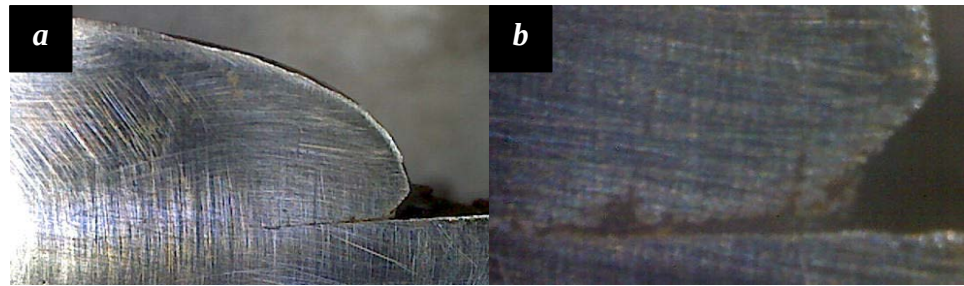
Probeta#2, Falla por soldadura fría, a:10x, b:20x
